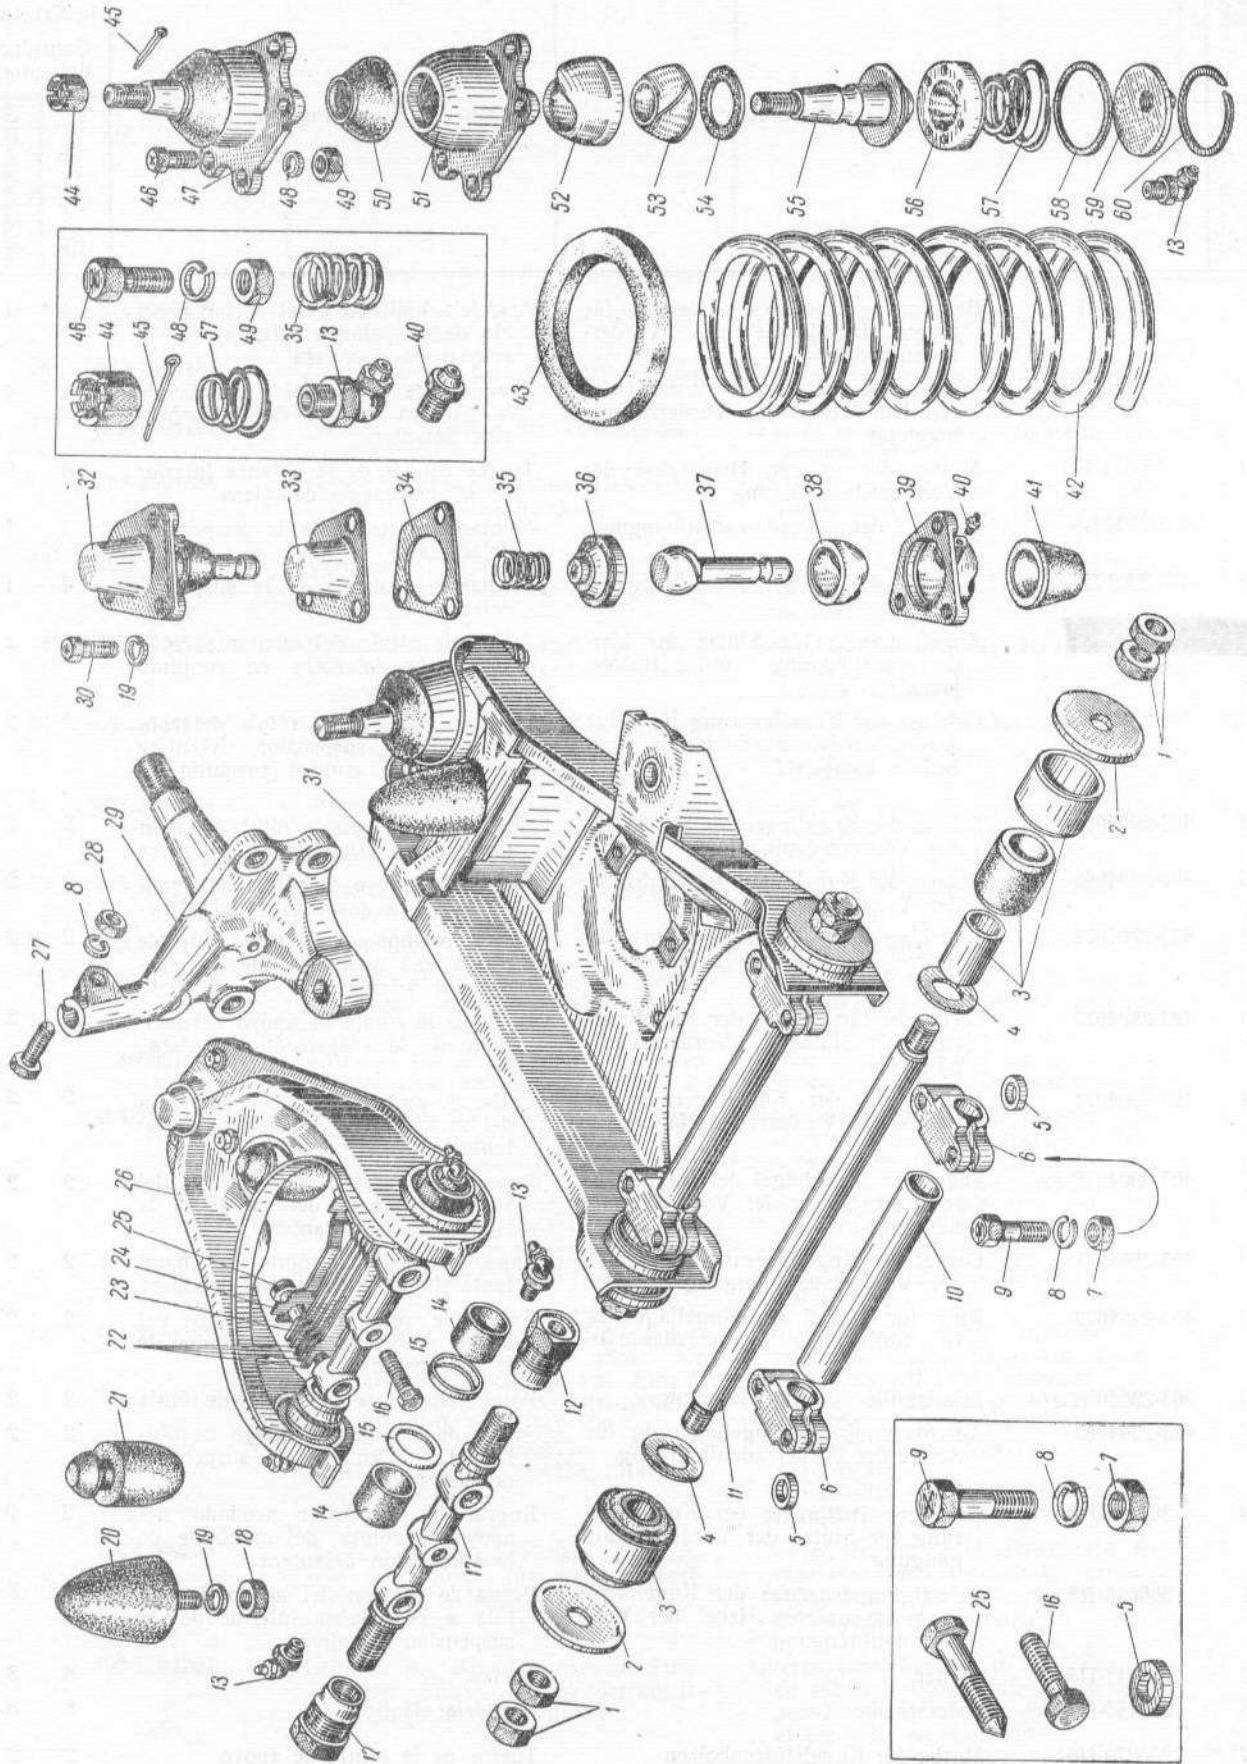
Feder, Stütze und Hebel der Vorderradaufhängung
